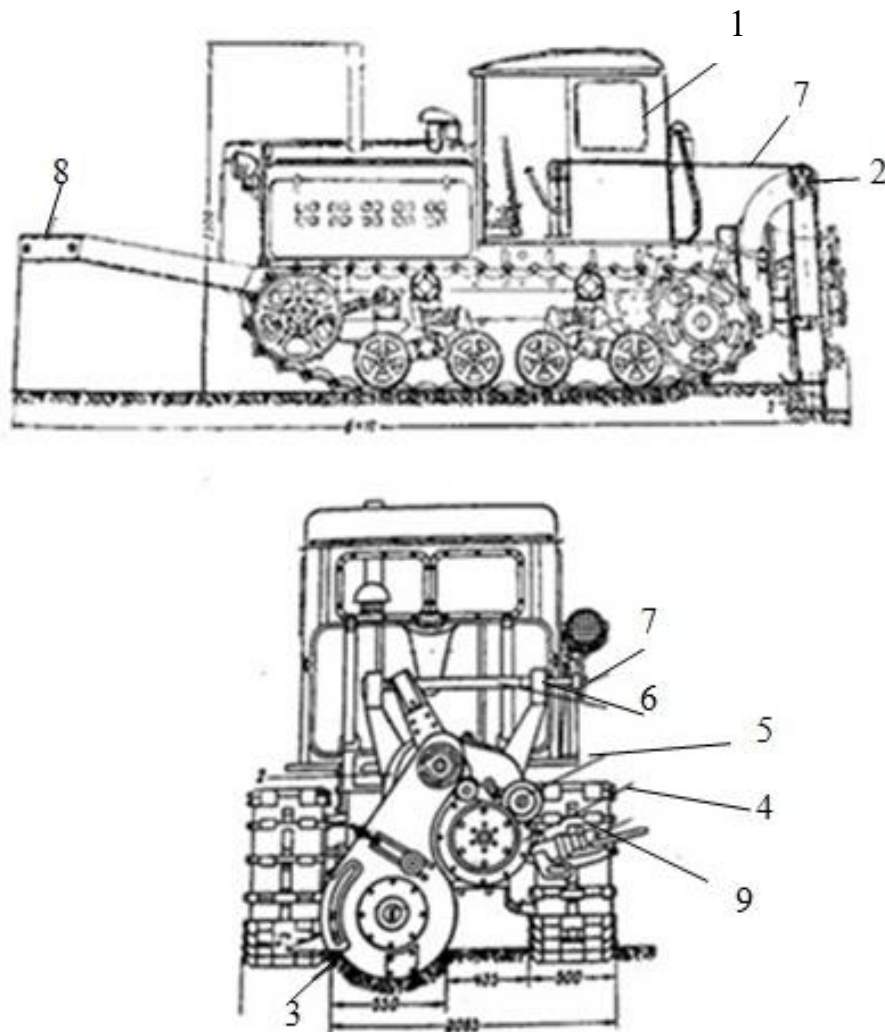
Общий вид машины КДН-2: 1 – кабина гусеничного трактора; 2 – редуктор цилиндрический; 3 – фреза; 4 – кожух щелевого пресса; 5 – загрузочный барабан щелевого пресса; 6 – винтовой механизм подъема и опускания фрезы; 7 – цепная передача на винтовой механизм подъема и опускания рабочего органа; 8 – контргруз; 9 – мундштук с укладкой торфа в валок
